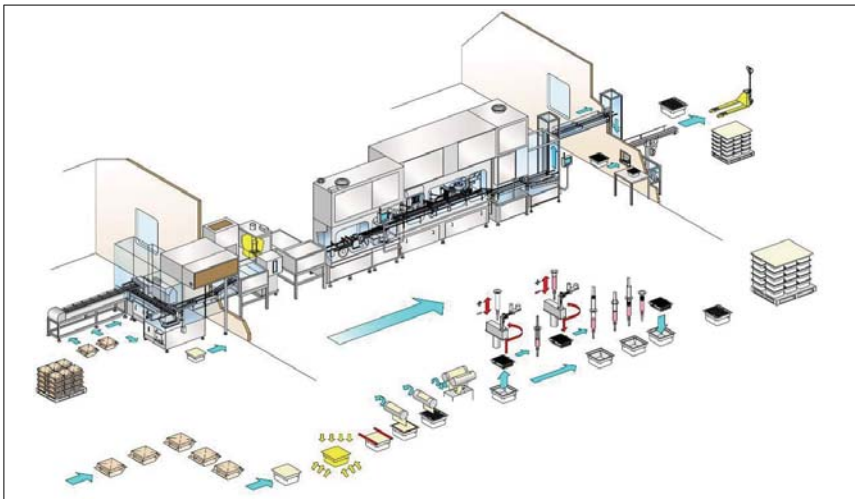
Prinzipskizze einer Füll- und Verpackungsmaschine
